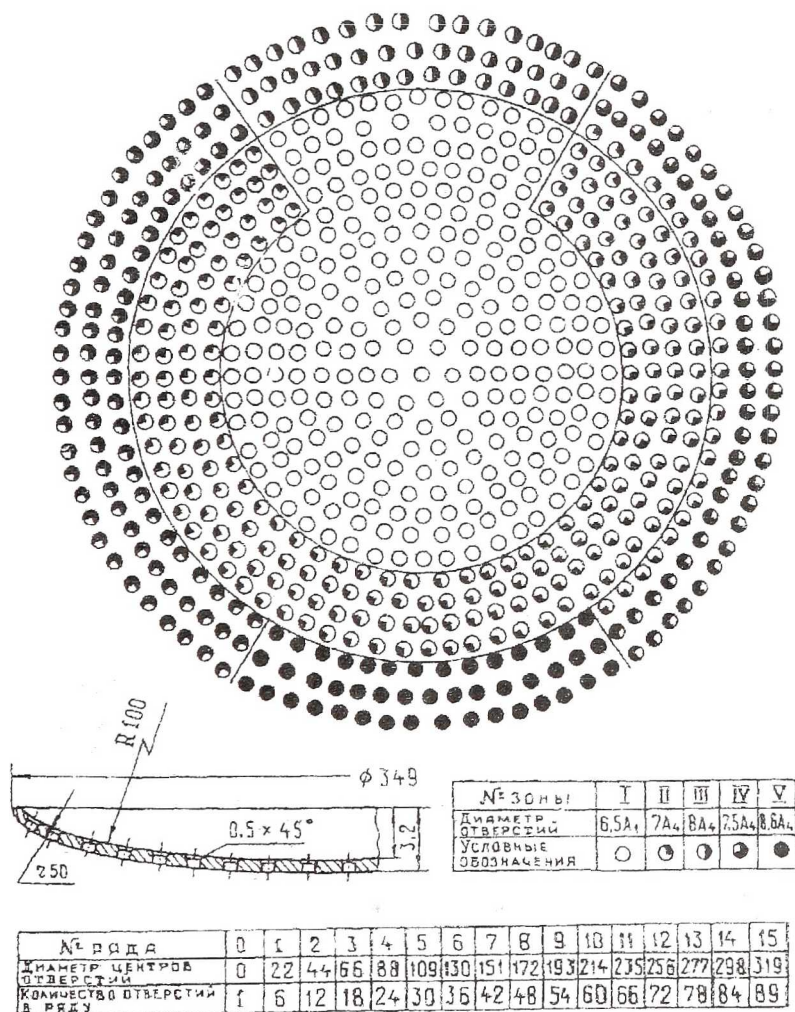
Схема расположения отверстий выравнивающей решетки КС двигателя НК-33
